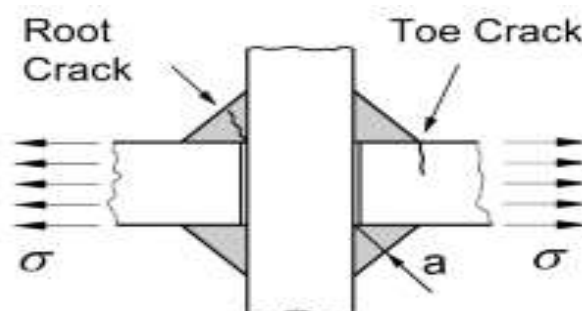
Localisation des éventuelles fissures dans un assemblage cruciforme avec des soudures d'angle
